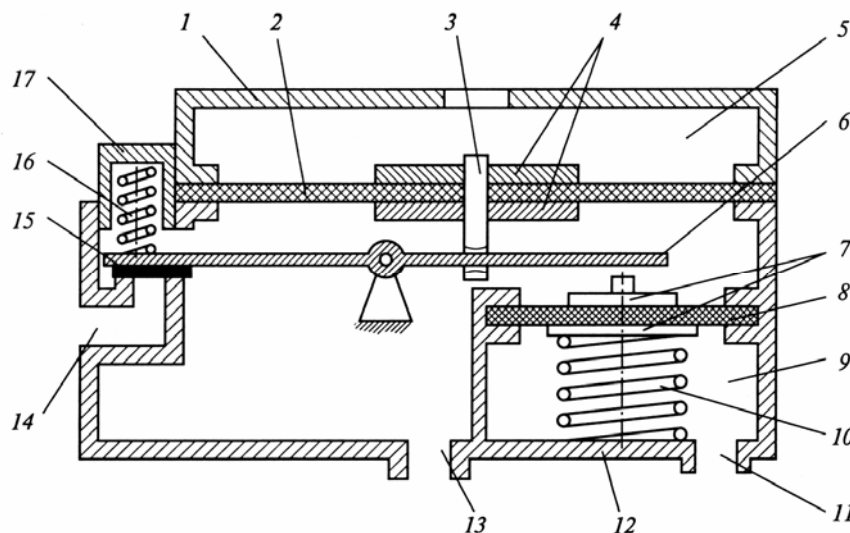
Принципиальная схема 2-й ступени редуктора:
